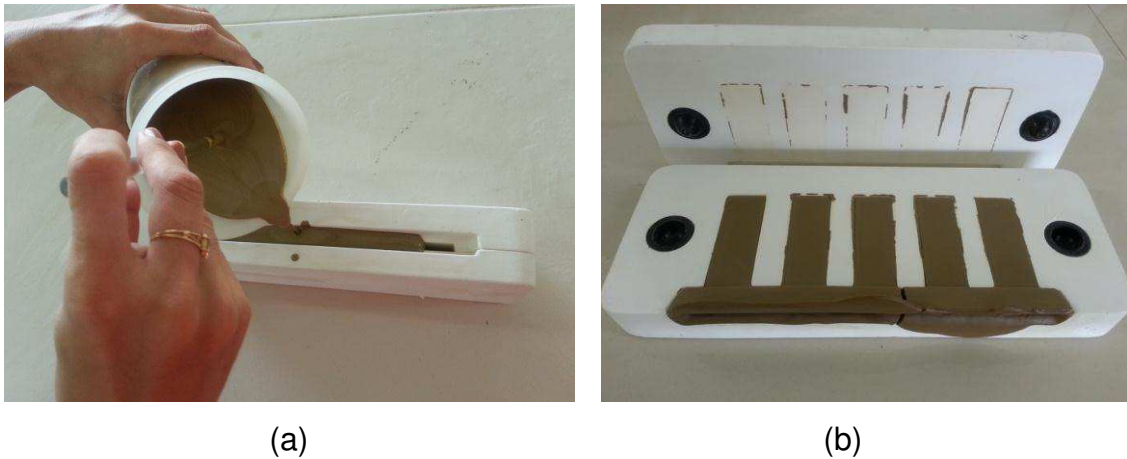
Processo de colagem em molde de gesso (a); corpos de prova (b)
